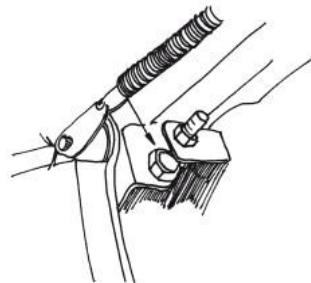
Зазор между толкателем и поршнем главного цилиндра гидропривода
